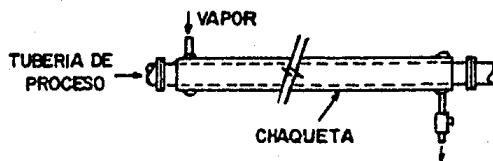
ENCHAQUETADO DE UNA TUBERIA DE PROCESO.
